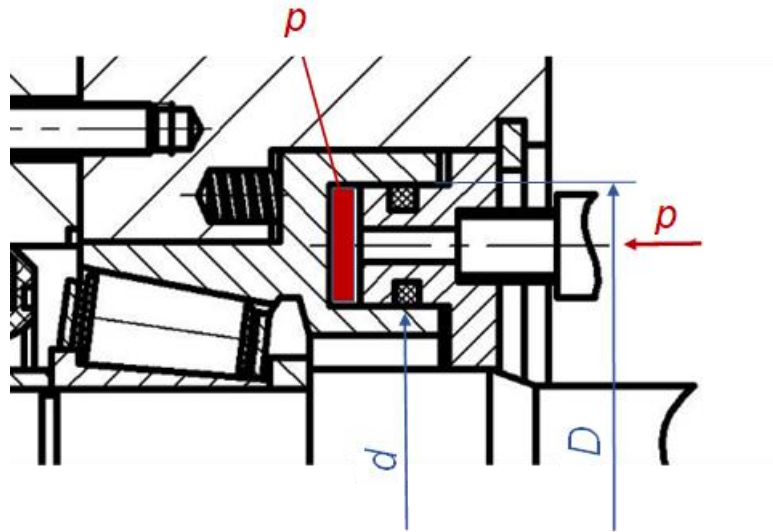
Розрахункова схема для визначення осьової сили натягу
